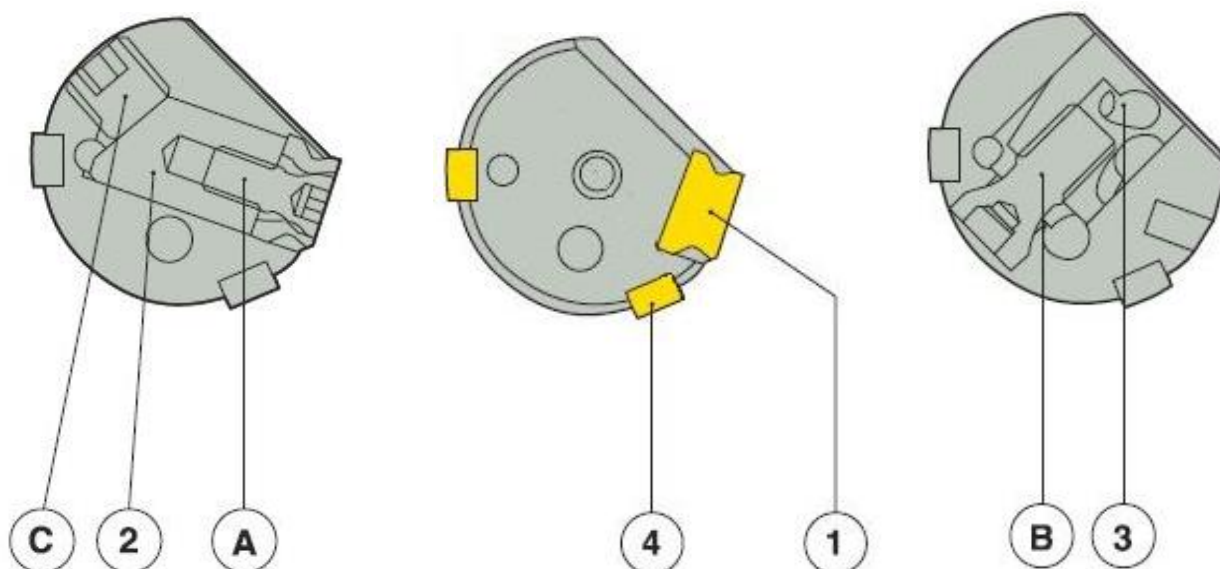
Схема головки розвертки Precifix. 1 - пластина;
